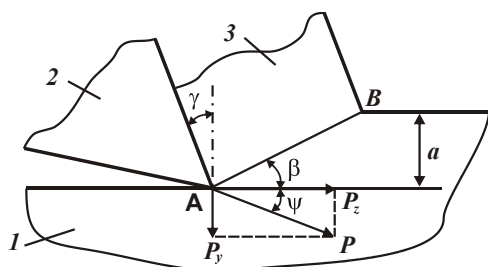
Расчетная схема процесса резания: 1 – обрабатываемый материал; 2 – резец; 3 – стружка
